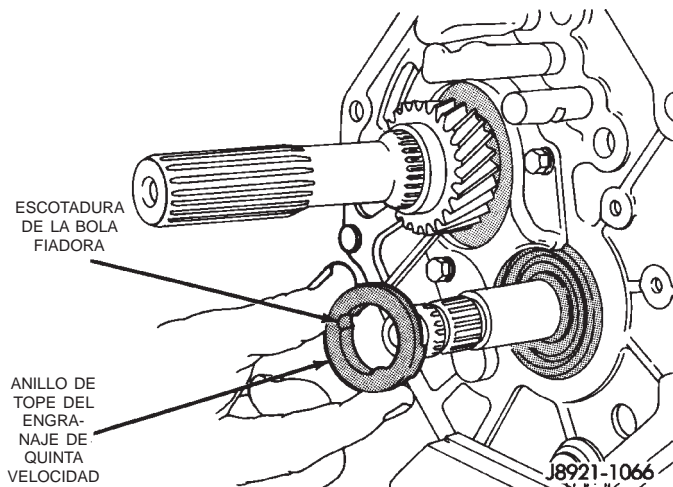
Desmontaje del anillo de empuje del engranaje de quinta velocidad
